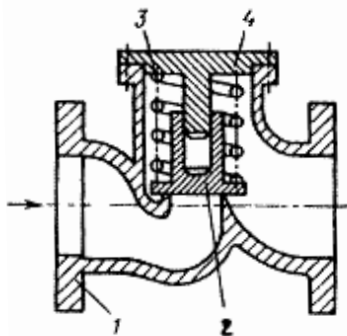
Обратный клапан: 1 – корпус; 2 – золотник; 3 – пружина; 4 – крышка
